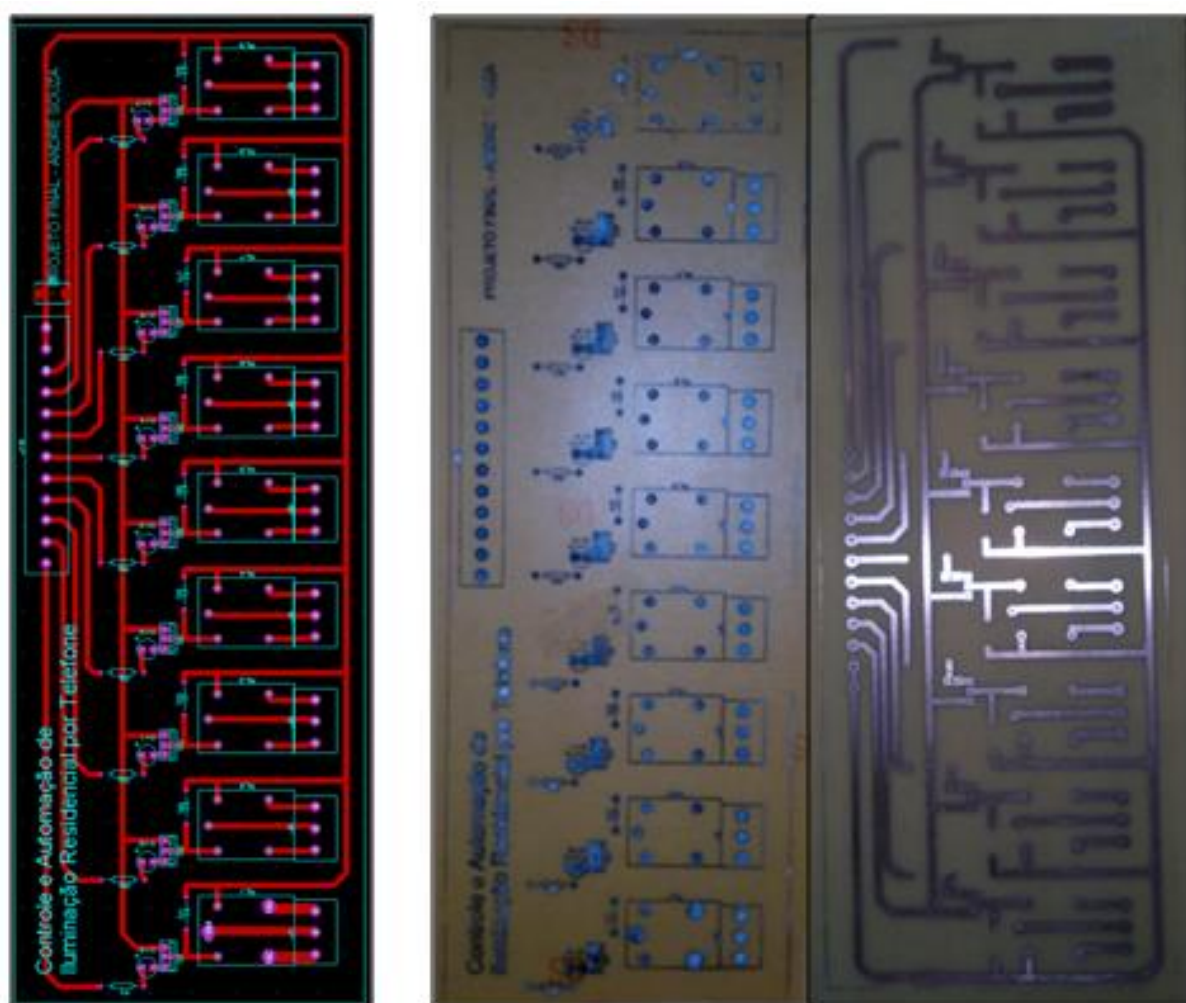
Desenho da Placa de Relés e Placa descobreada pronta. (AUTOR)
